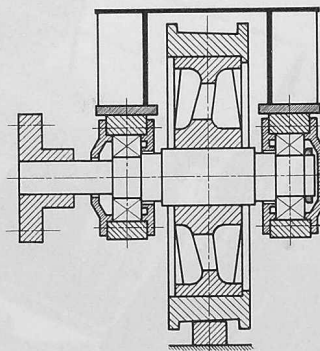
Angetriebene Rolle eines Kranfahrwerks mit Wälzlagern. Das Rad ist auf der Achse aufgepresst. Sie ruht in Wälzlagern. Antrieb durch die Kupplung. Zweiteilige Rolle mit konischer Lauffläche
